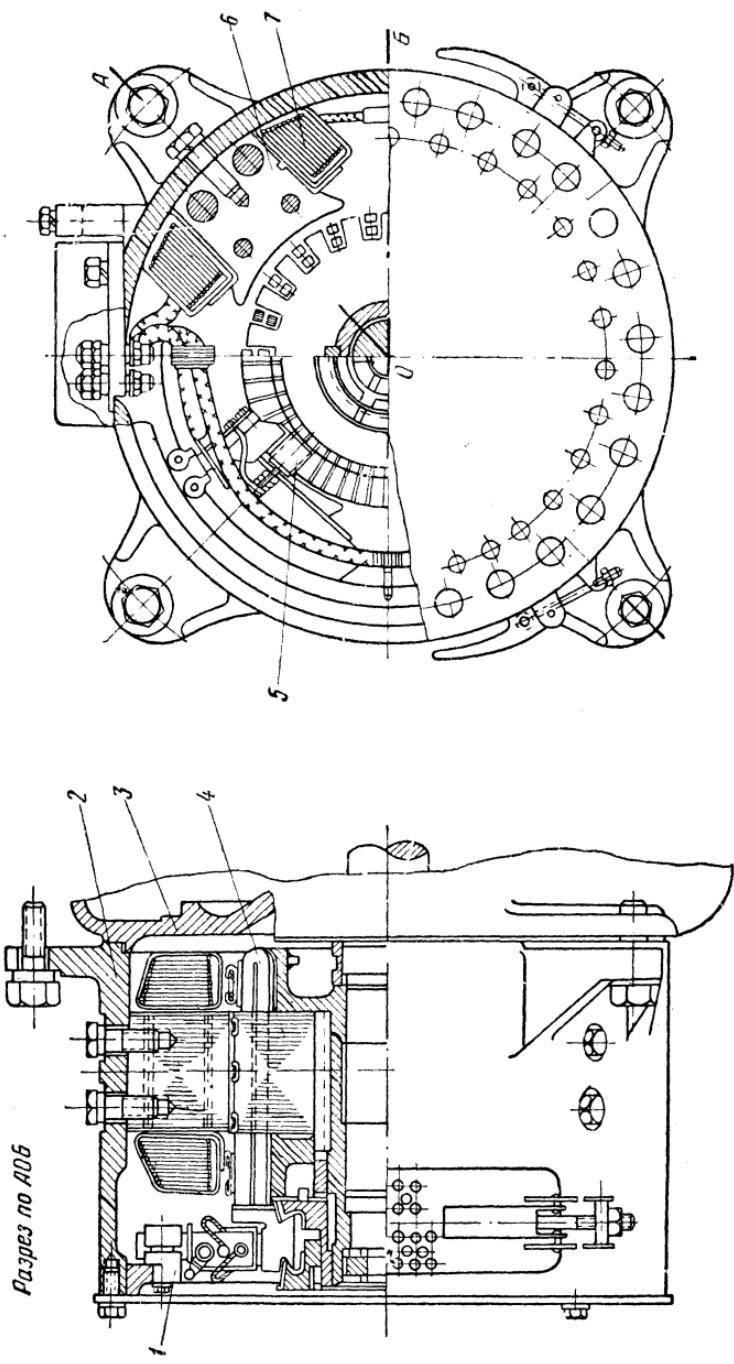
Продольный и поперечный разрезы генератора управления ДК-405К:
